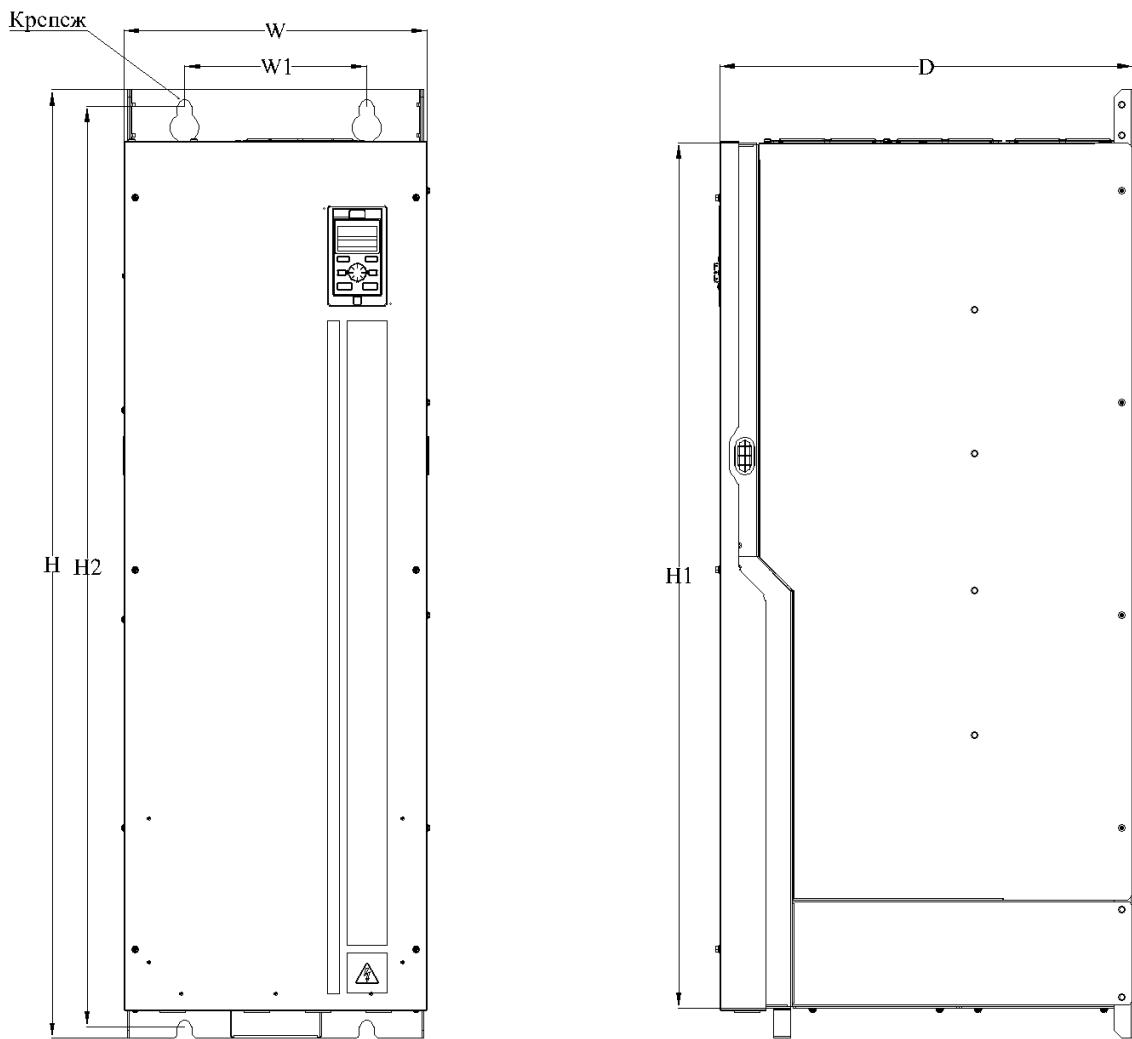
Чертеж преобразователя частоты типоразмер 10
